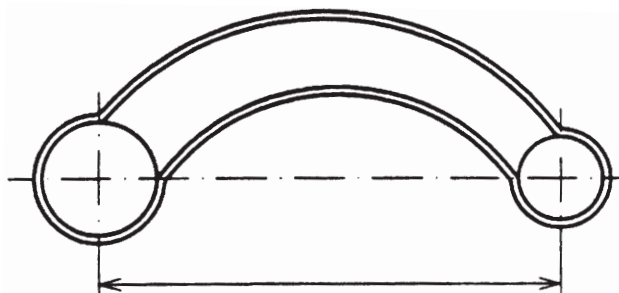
Maß, für welches die Toleranzen für Mittenabstände nicht angewandt werden dürfen
